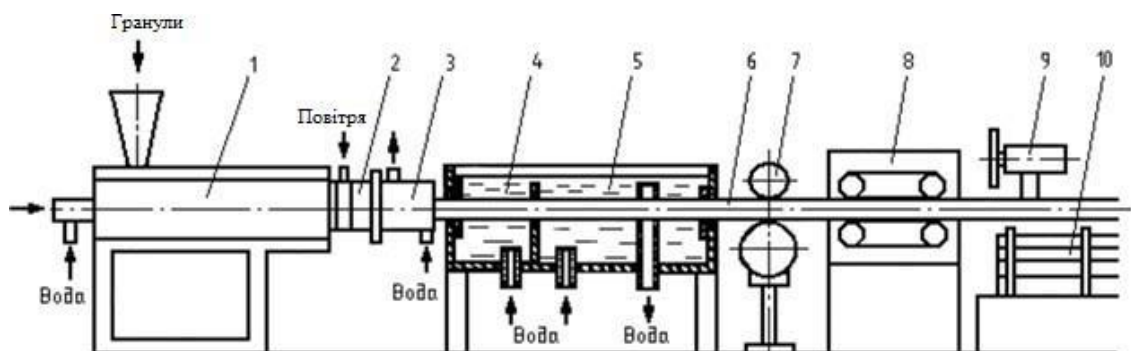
Схема агрегату для виробництва труб методом екструзії, де 1 - екструдер; 2 - формуюча головка; 3 - калібруюча насадка; 4, 5 - перша і друга зони охолодження; 6 - трубчастий профіль; 7 - вимірювально маркуючий пристрій; 8 - тягнучий пристрій; 9 - відрізаючий пристрій; 10 - приймальний стіл (штабелювальний пристрій)
